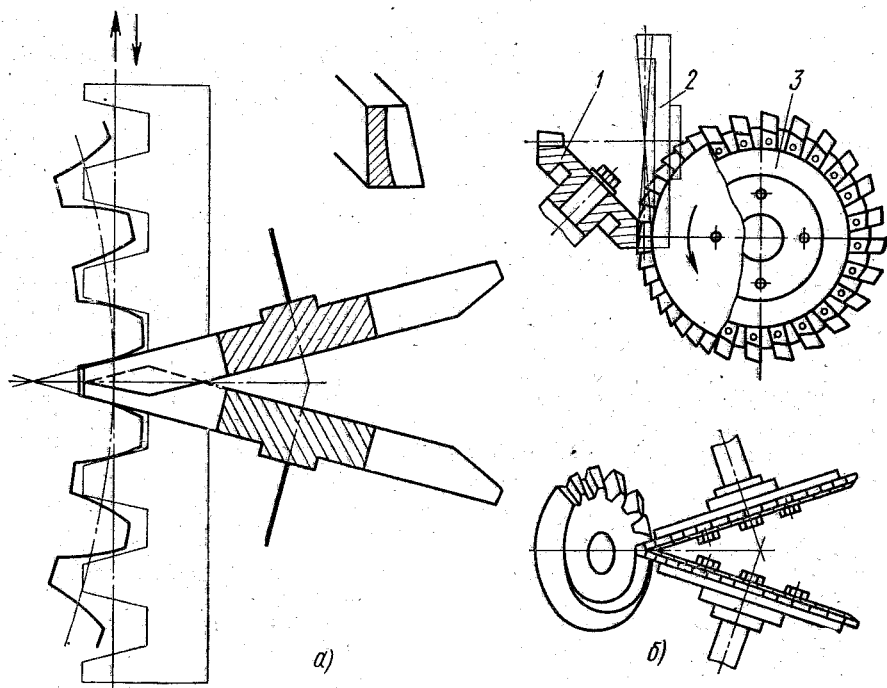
Схема нарезания прямозубого конического колеса двумя дисковыми фрезами по методу обкатки
